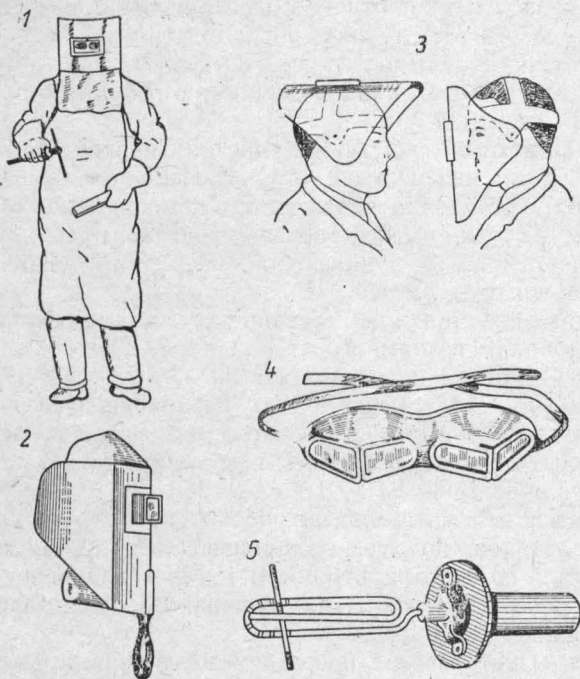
Защитные приспособления для электросварщиков:
